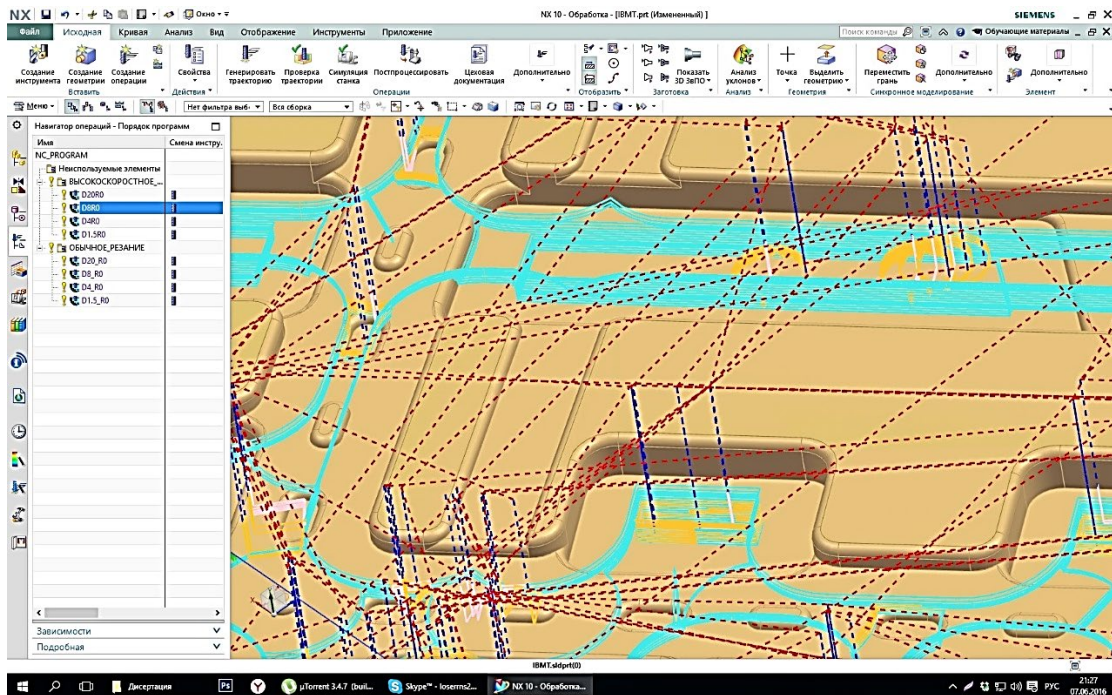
Траектория фрезы диаметром 8 при высокошвидкісному фрезеруванні
